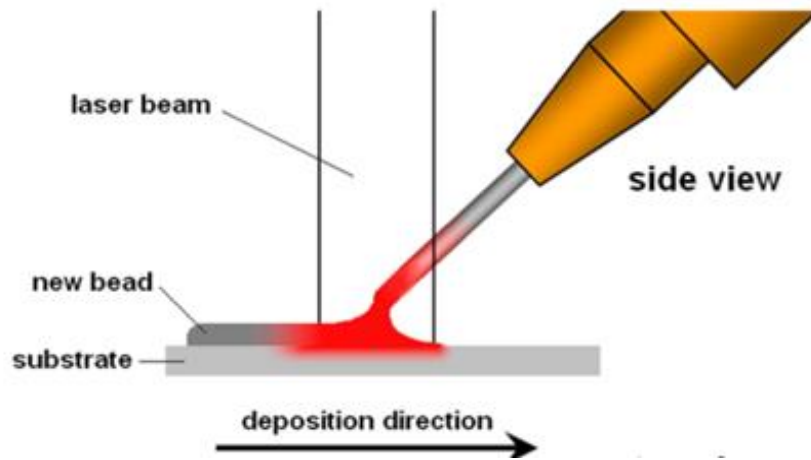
Laser Metal Deposition-wire. Fonte: [19]
